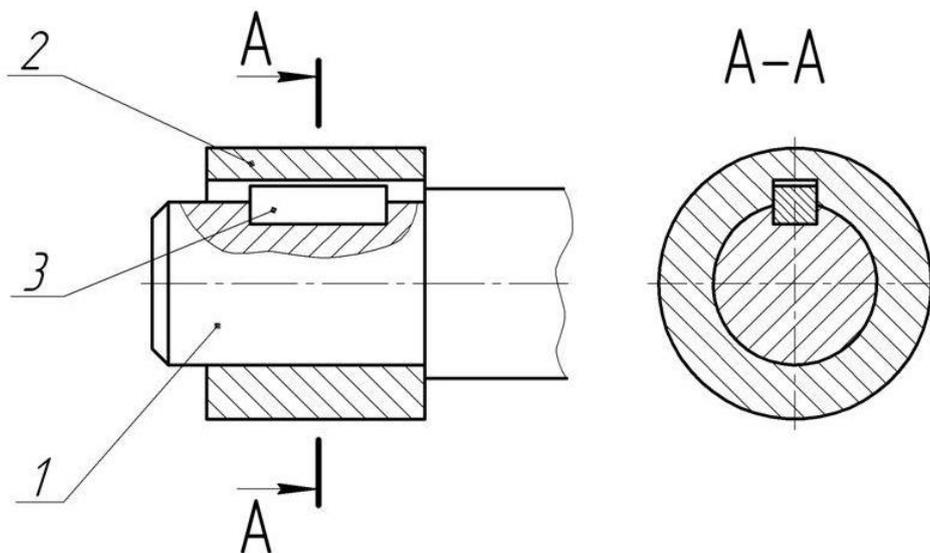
Соединений деталей при помощи шпонки призматической
